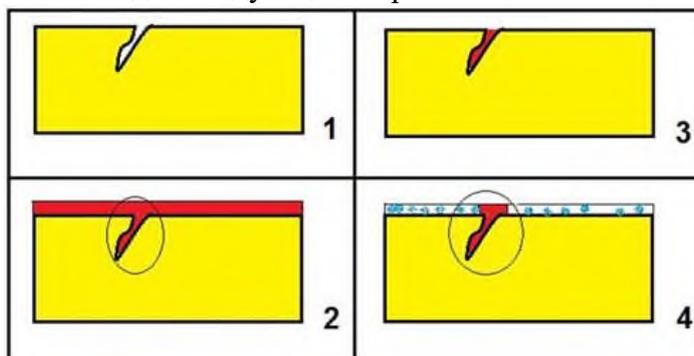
Контроль сварных соединений пенетрантом
